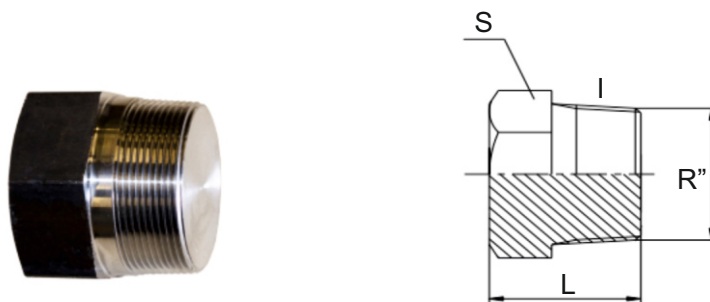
Заглушка для установки в муфту соединения РВД
